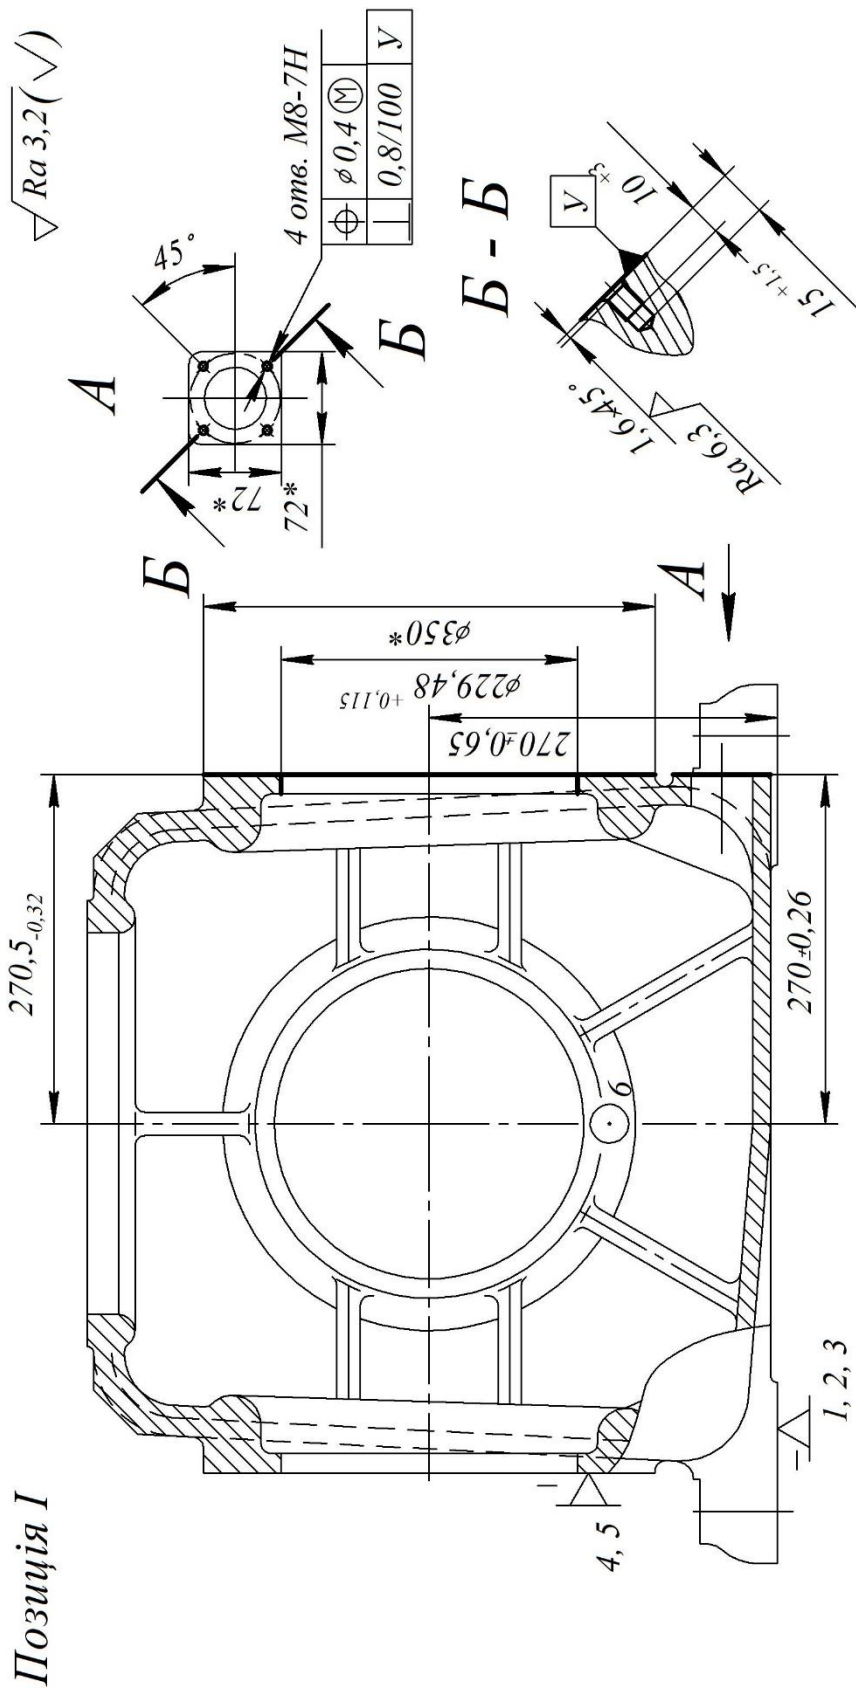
Альтернативна схема базування заготовки на фрезерно-свердильно-розточувальній операції 020
